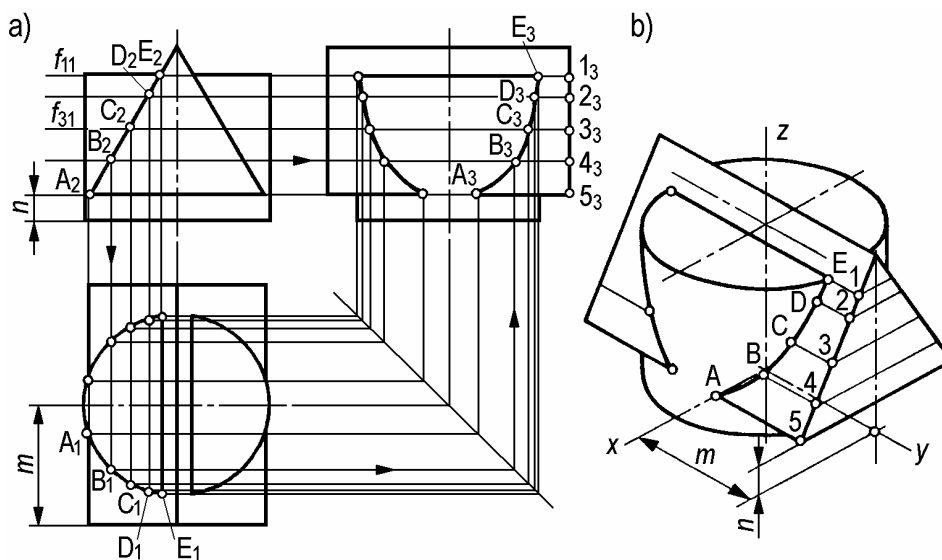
Prodor prizme i krnjeg stošca kao primjer za objašnjenje općih pravila konstruiranja crta presjeka (crta prodora) ploha
